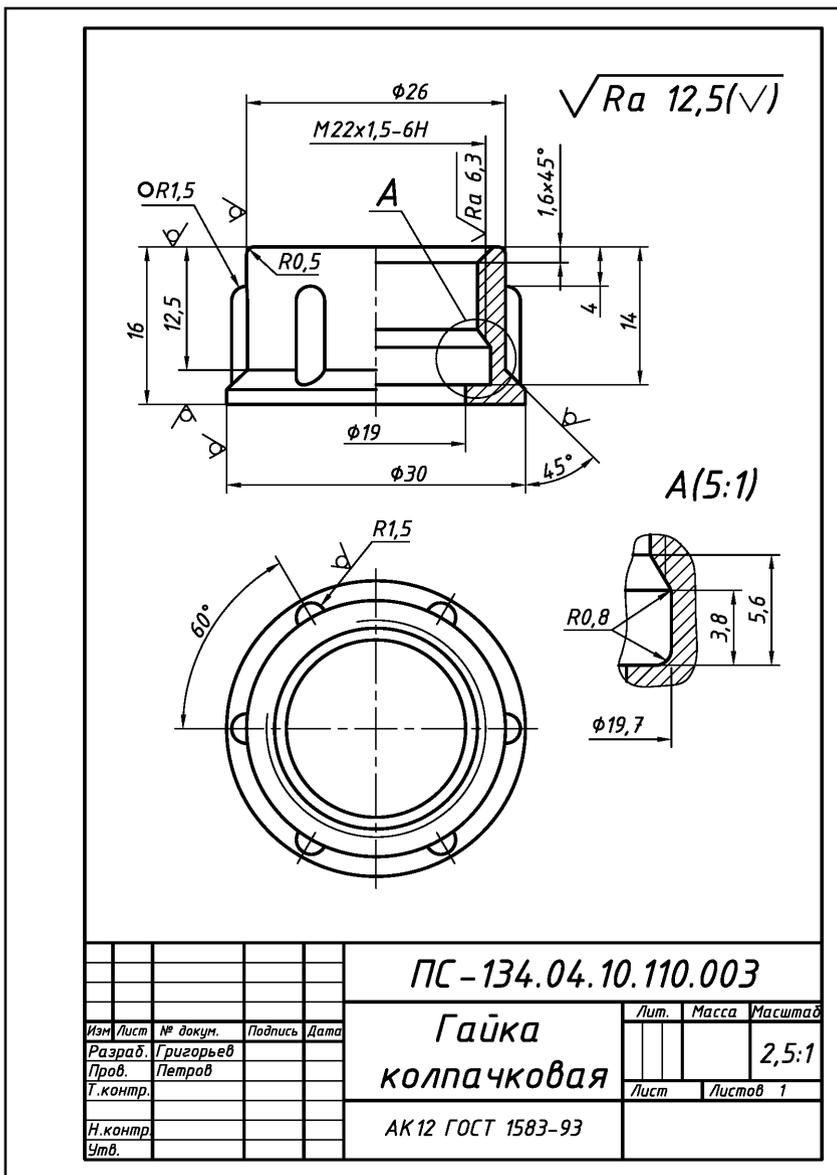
Оформление рабочего чертежа литой детали из металла с обработкой
